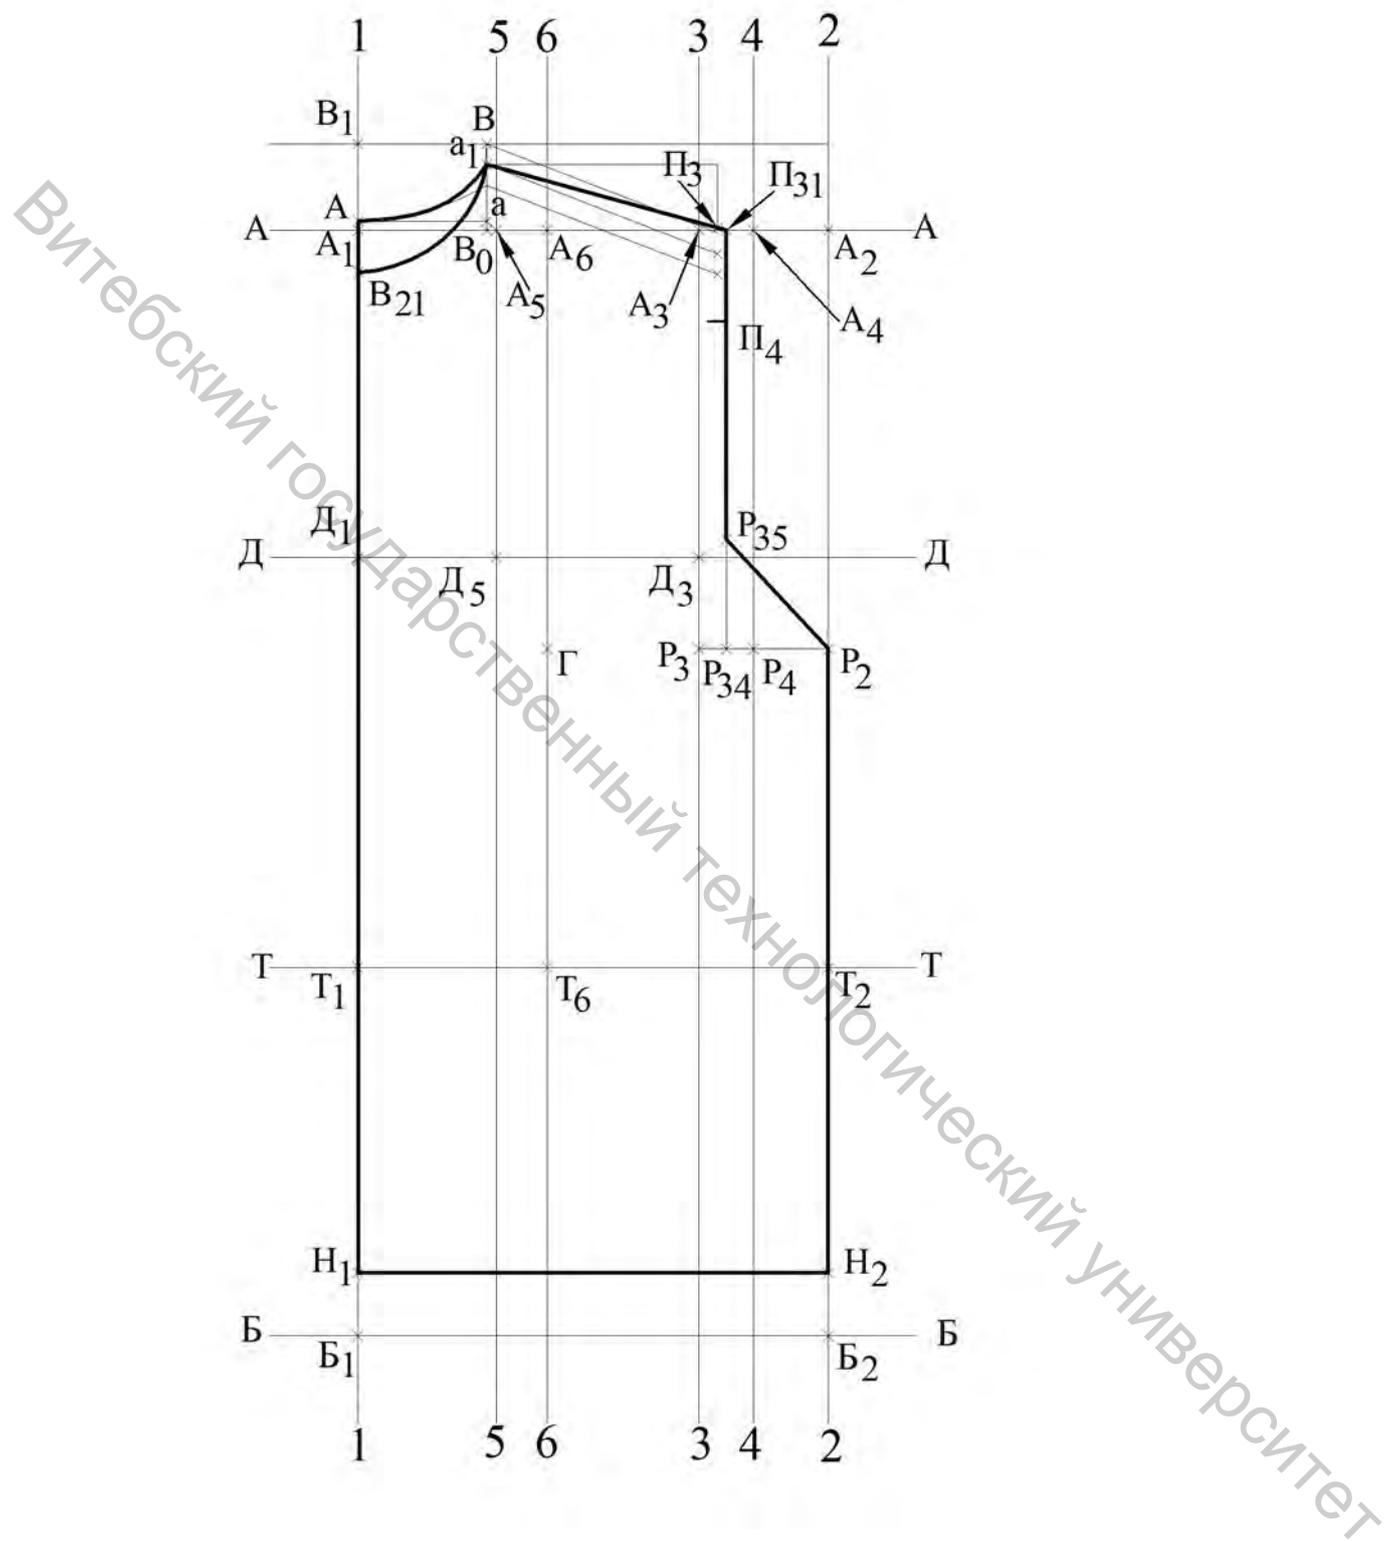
Чертеж конструкции деталей стана джемпера регулярного
